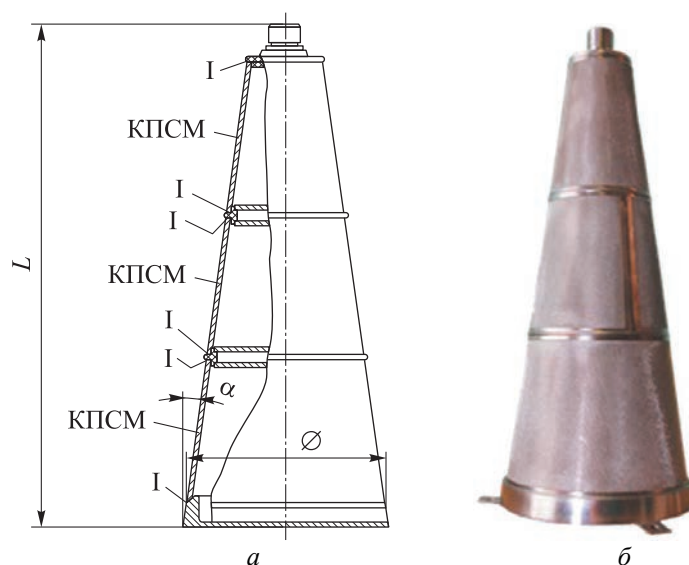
Конструктивная схема (а) и общий вид (б) фазоразделителя ДУ КА «Купон» на основе КПСМ (I — места лазерной сварки)
